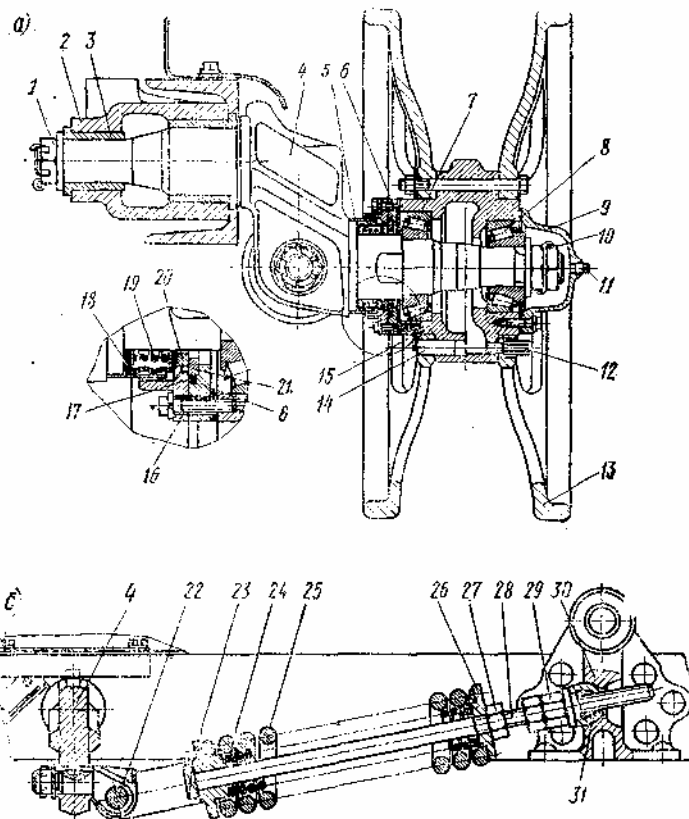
Направляющее колесо и натяжное устройство трактора ДТ-75
